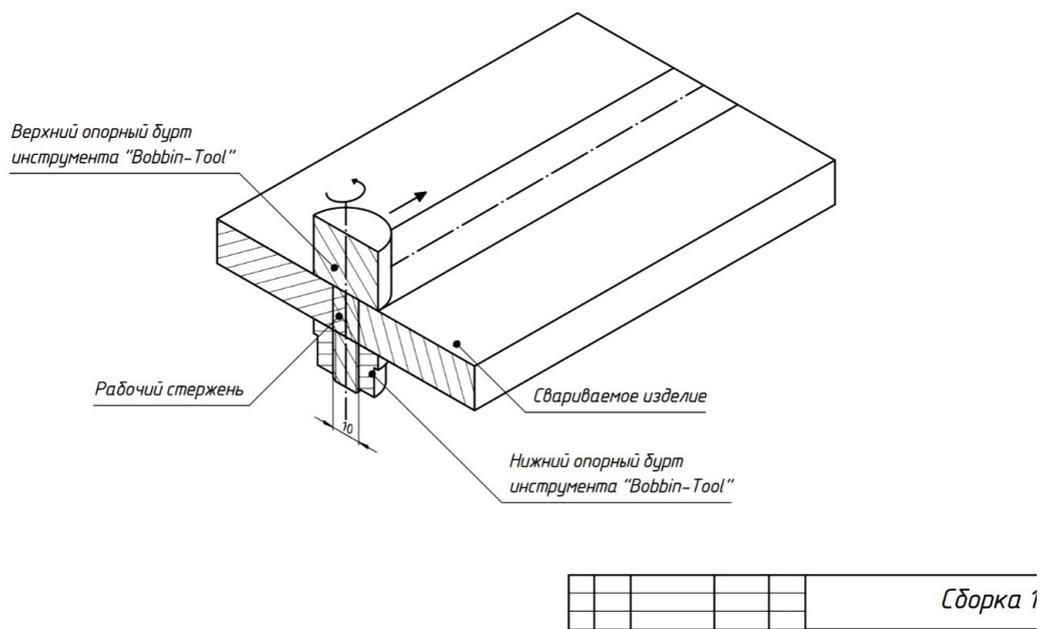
Схема процесса фрикционной сварки инструментом типа «Bobbin-Tool»
